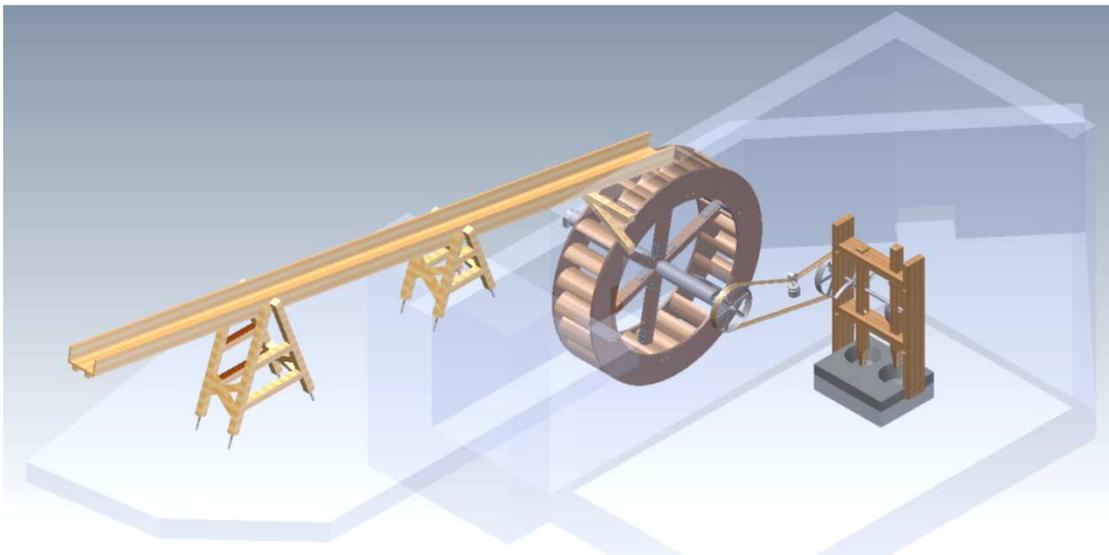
Planungsskizze von Wasserkanal, Wasserrad, Antrieb und Stampfe (v.l.n.r.).
